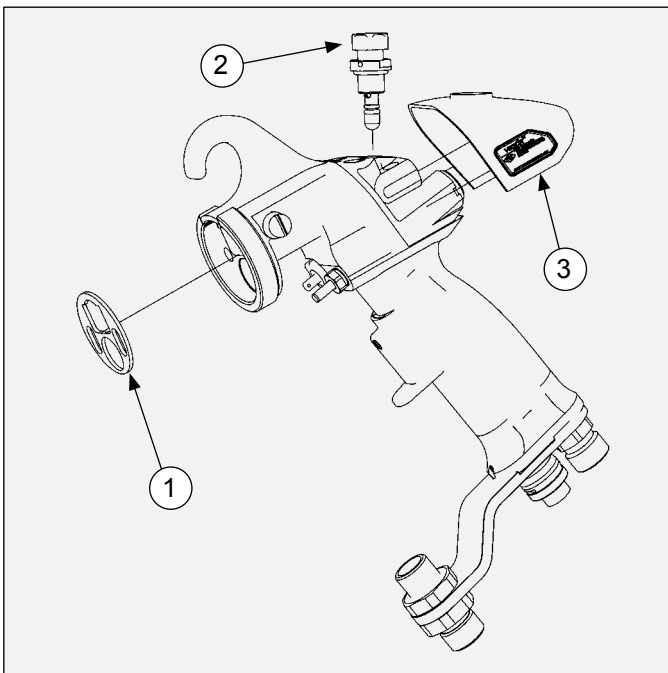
Desmontaje de la válvula de aire y cubierta trasera
